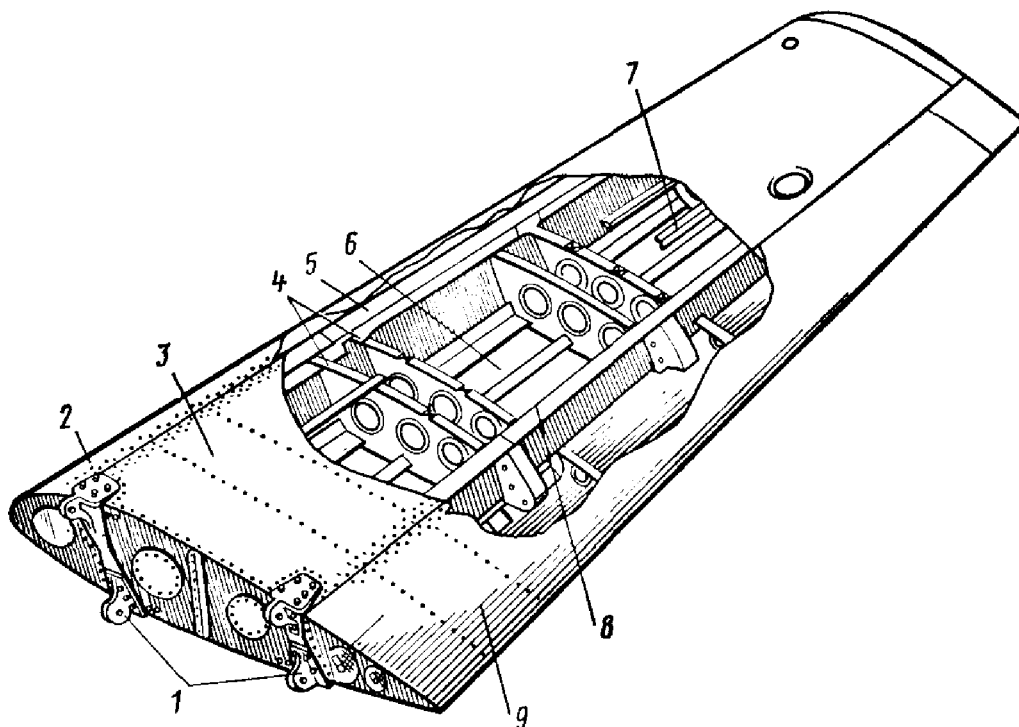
Конструкция консоли крыла вертолета Ми-6 [6]:
